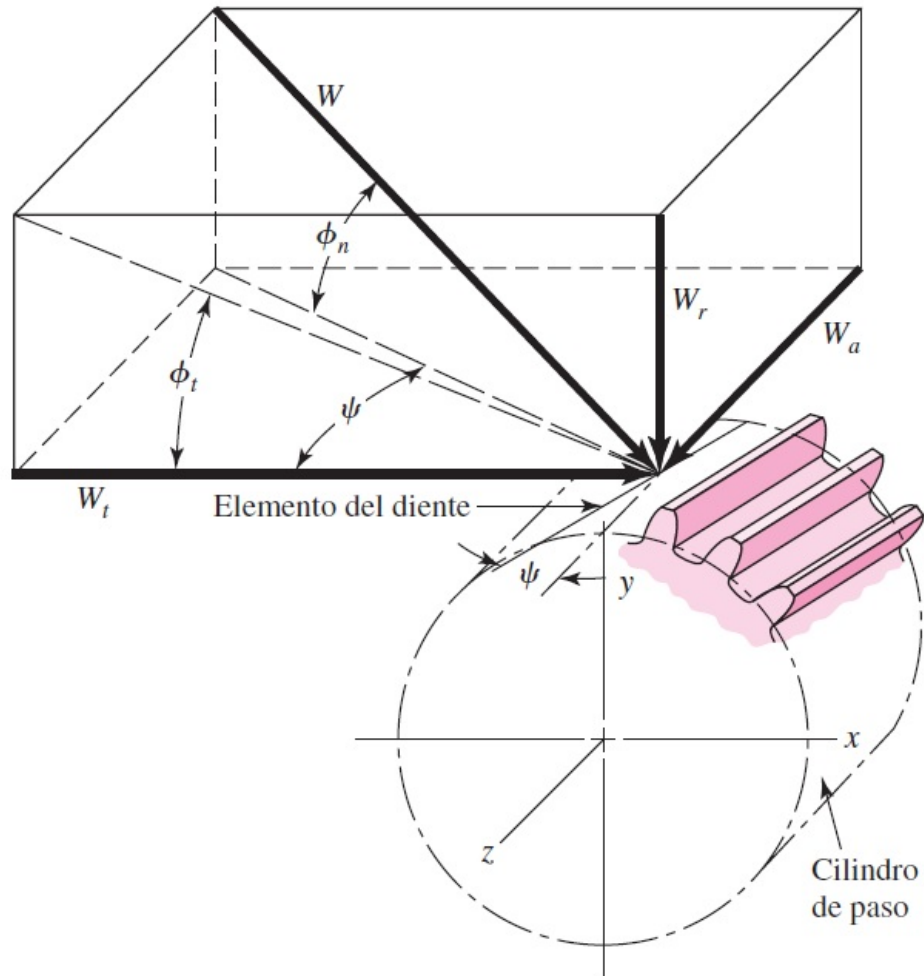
Fuerzas que actúan en el diente de un engrane helicoidal [9].
